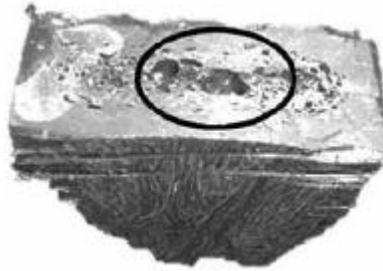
Muestra de plástico extruido, presencia de grietas y vacíos. (SALAZAR Edgar, 2014)
